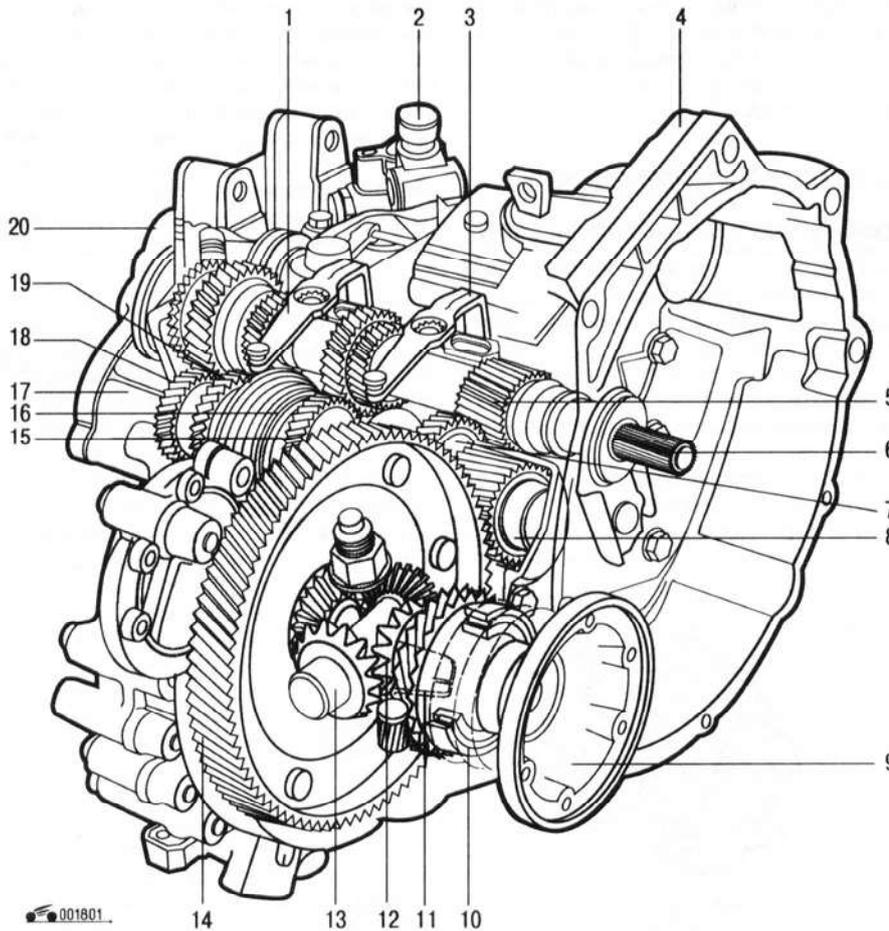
Механическая коробка передач: 1 – вилка включения III и IV передач; 2 – механизм выбора передач; 3 – управление переключением передач; 4 – картер сцепления; 5 – шестерня первичного вала; 6 – первичный вал; 7 – шестерня I передачи; 8 – вторичный вал; 9 – фланец привода; 10 – конический подшипник дифференциала; 11 – шестерня привода спидометра; 12 – полуосевая шестерня; 13 – ось сателлитов; 14 – ведомое зубчатое колесо главной передачи; 15 – шестерня II передачи; 16 – шестерня III передачи; 17 – картер коробки передач; 18 – шестерня V передачи; 19 – шестерня IV передачи; 20 – задняя крышка картера коробки передач
